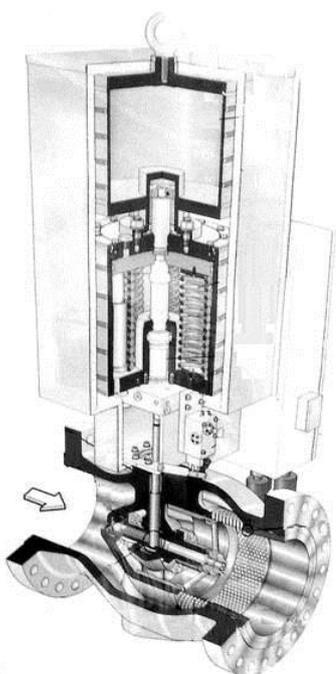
Антипомпажный клапан фирмы «Mokveld Valves» [22]
